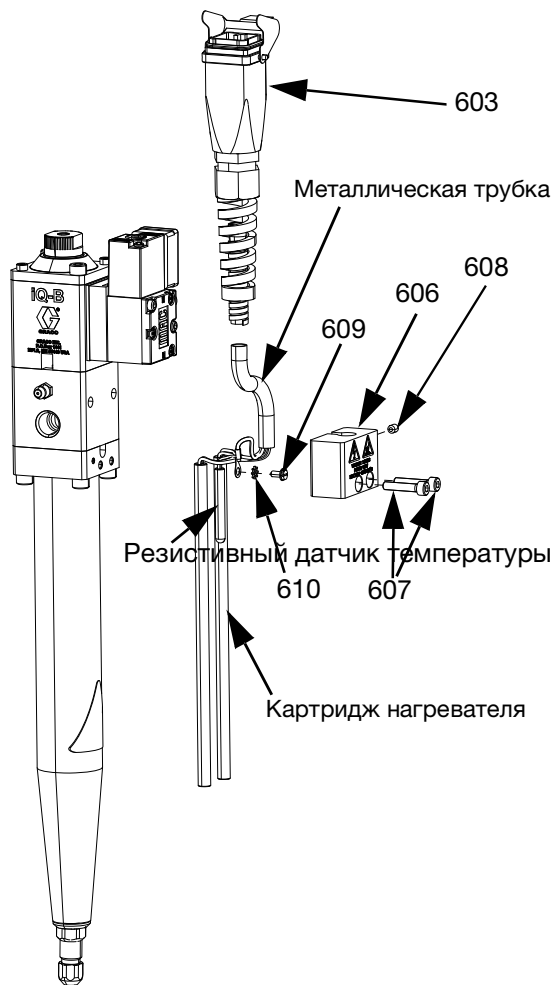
Нагреватель в сборе для выпускного блока 200 мм
